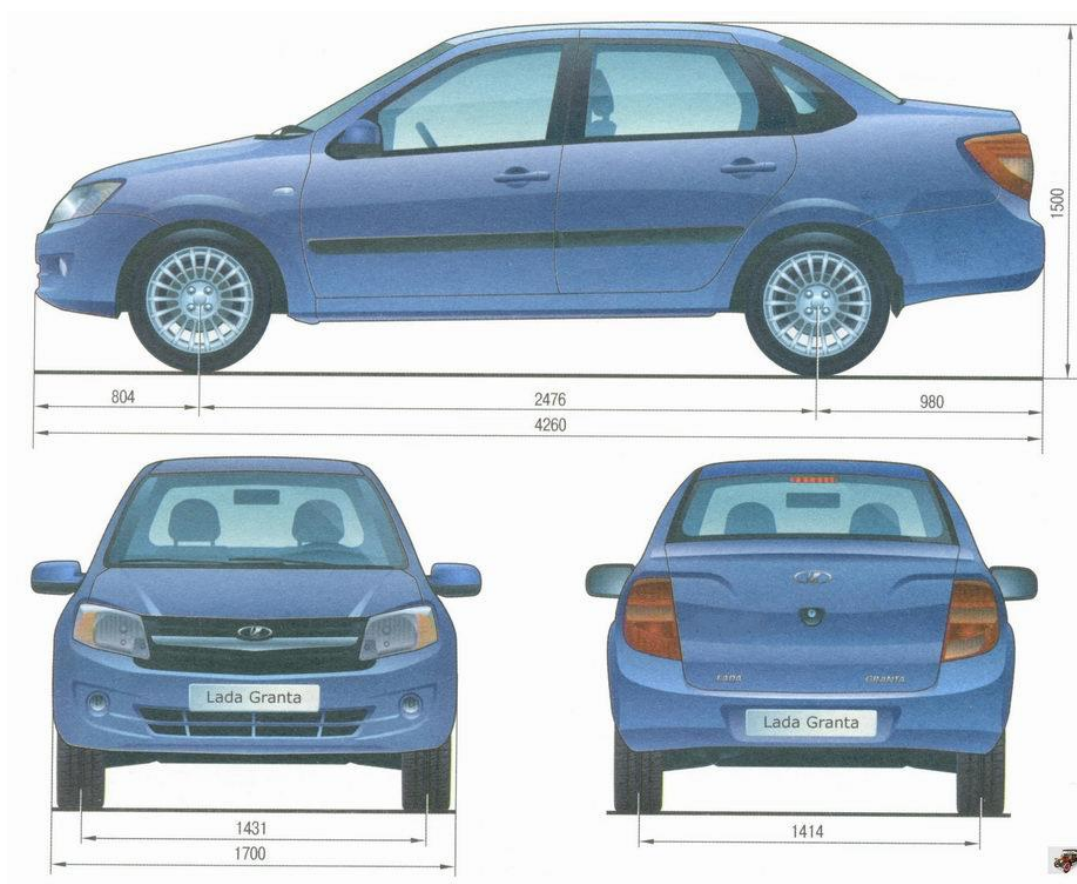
Внешний вид и габаритные размеры автомобиля Лада Гранта ВАЗ-2190
